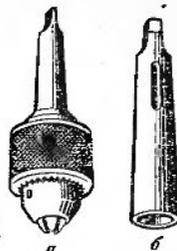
Приспособления для крепления сверл в шпинделе сверлильного станка:
